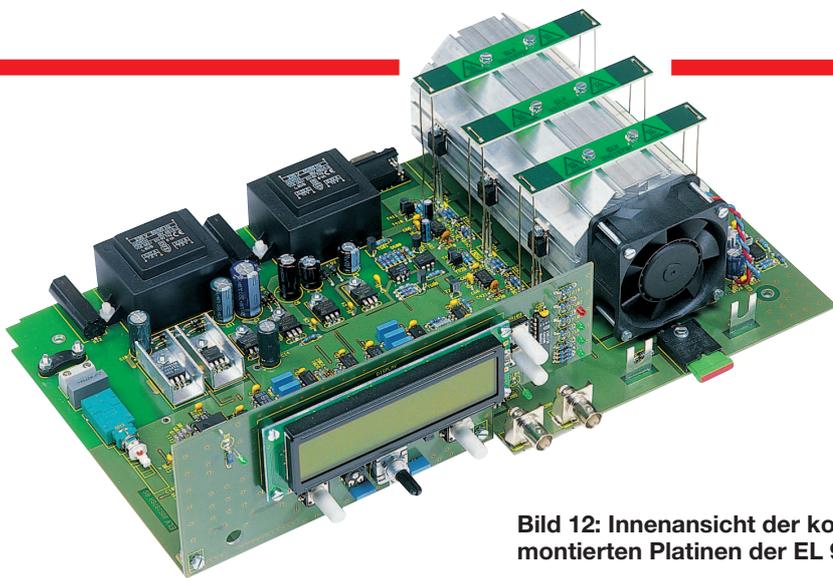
Innenansicht der komplett montierten Platinen der EL 9000
